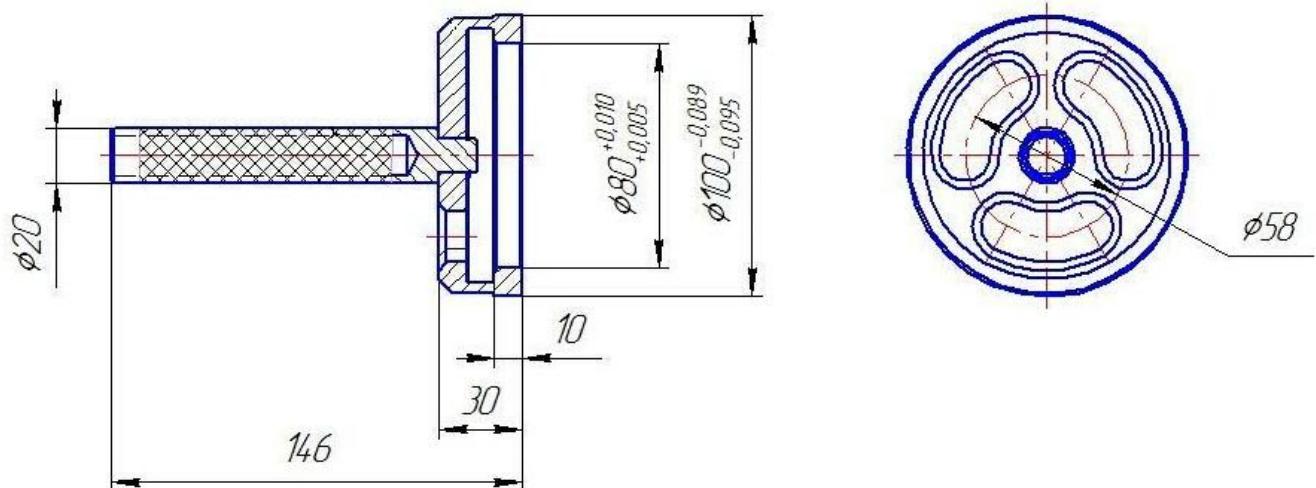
ЗМ 7853-4418, Оправка для центрирования заднего сальника в сборе с сальникодержателем относительно заднего фланца коленчатого вала
